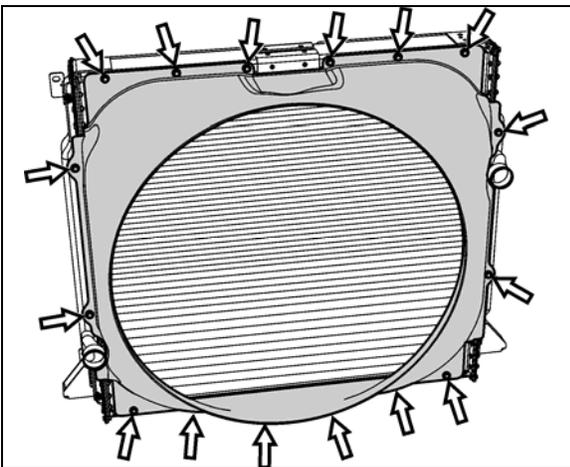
DÉMONTAGE DU CARÉNAGE DU VENTILATEUR
